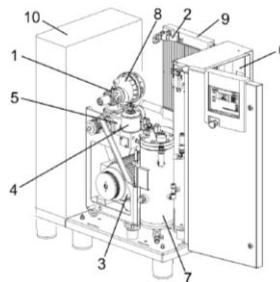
Конструкция компрессора: 1 – впускной клапан; 2 – обратный клапан минимального давления; 3 – двигатель компрессора; 4 – масляный фильтр; 5 – компрессорный блок; 6 – распределительный шкаф; 7 – маслоотделитель; 8 – воздушный фильтр; 9 – масляный и воздушный радиатор; 10 – шкаф для холодоосушителя
